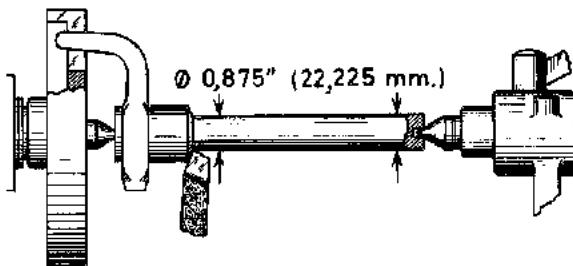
La pieza que se cilindra debe ser de diámetro uniforme.
